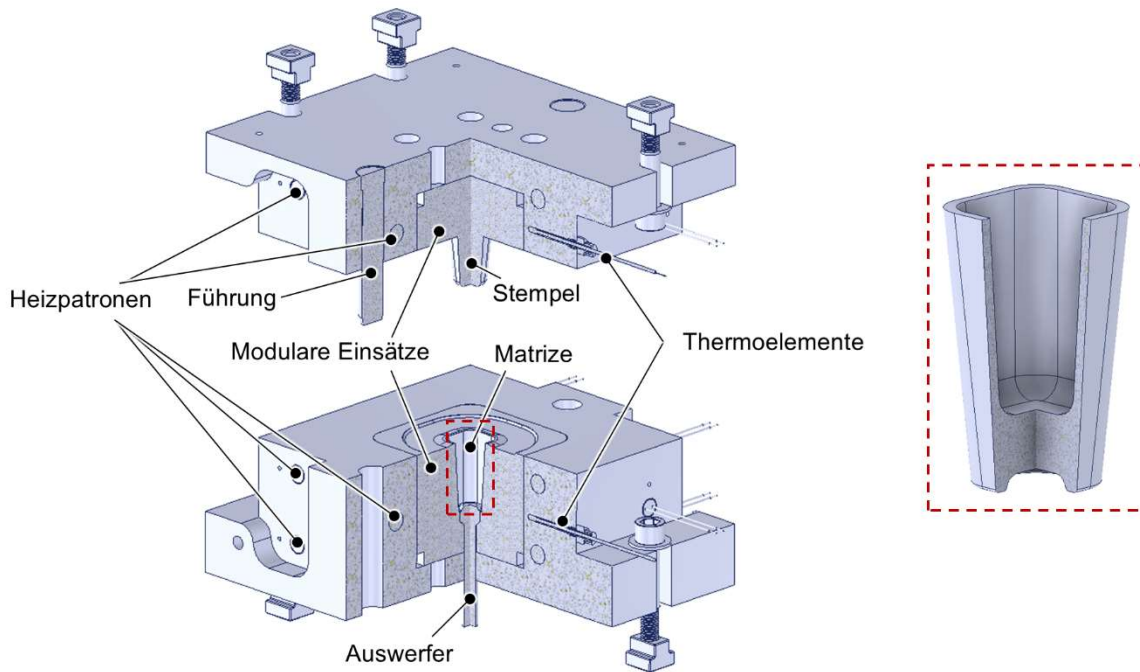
CAD-Zeichnung des Gesenkschmiedewerkzeugs und des Bauteils.
